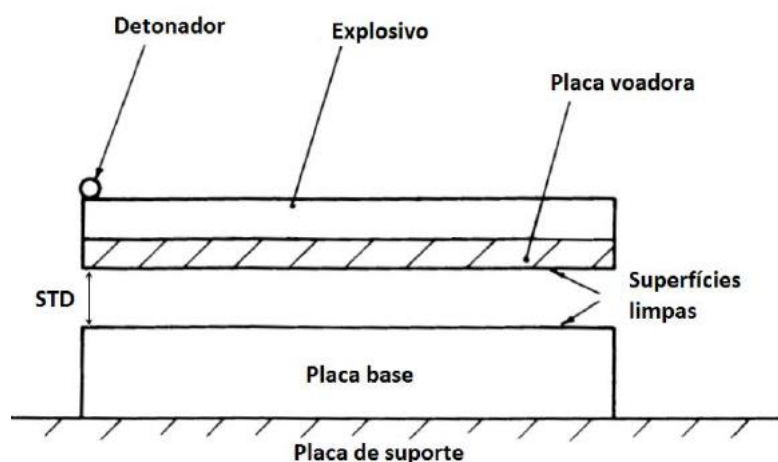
Configuração paralela do processo de soldadura por explosão, adaptada de Blazynsky [6].
